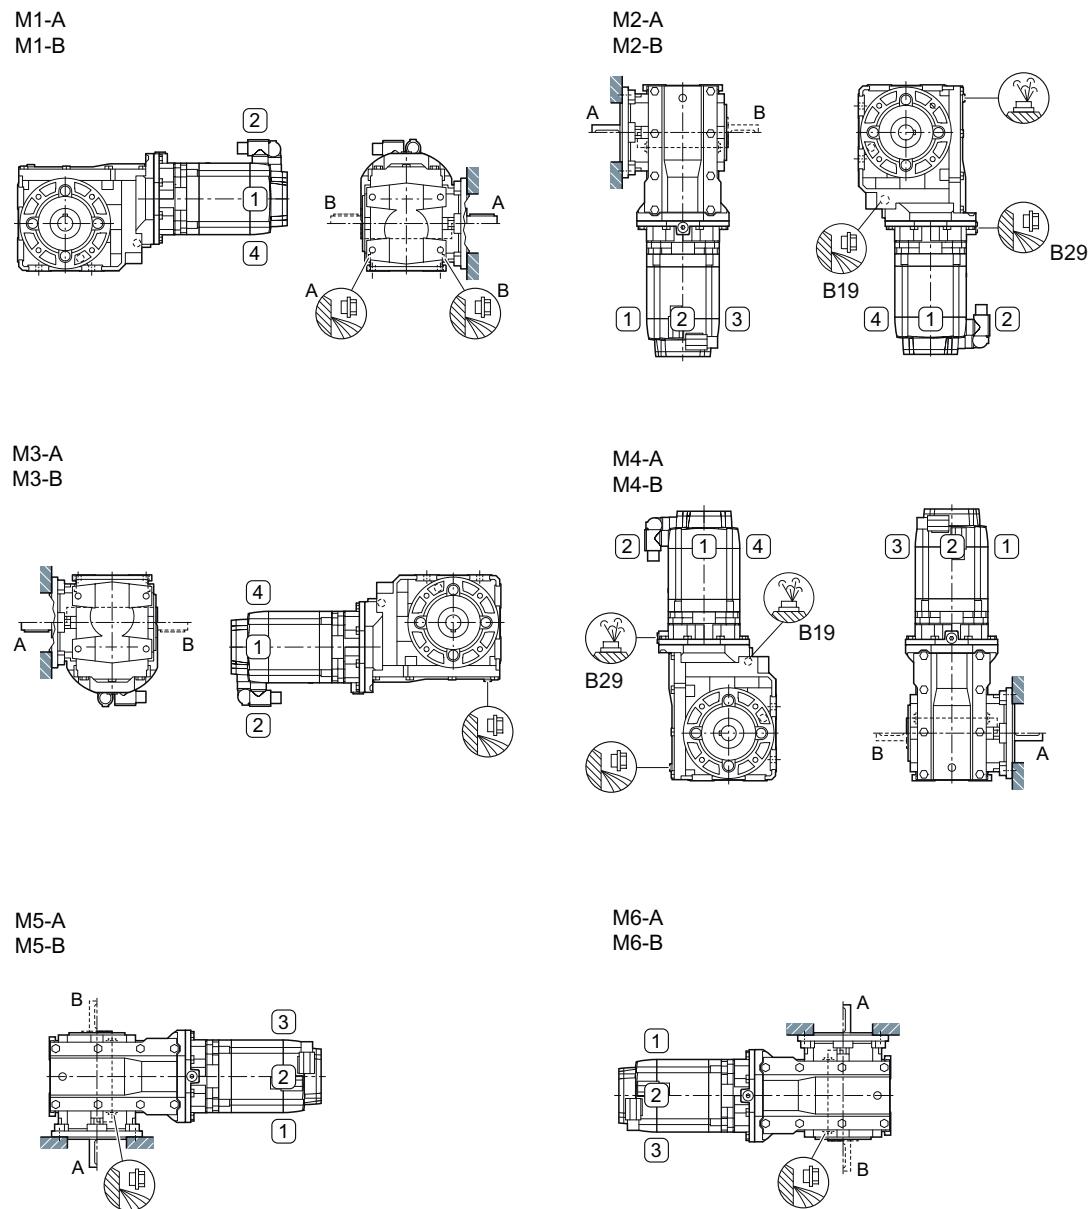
Einbaulagen für Servo-Kegelradgetriebemotor B.F (Flanschausführung) oder B.Z (Gehäuseflanschausführung), Baugrößen 19 - 29, 2-stufig
